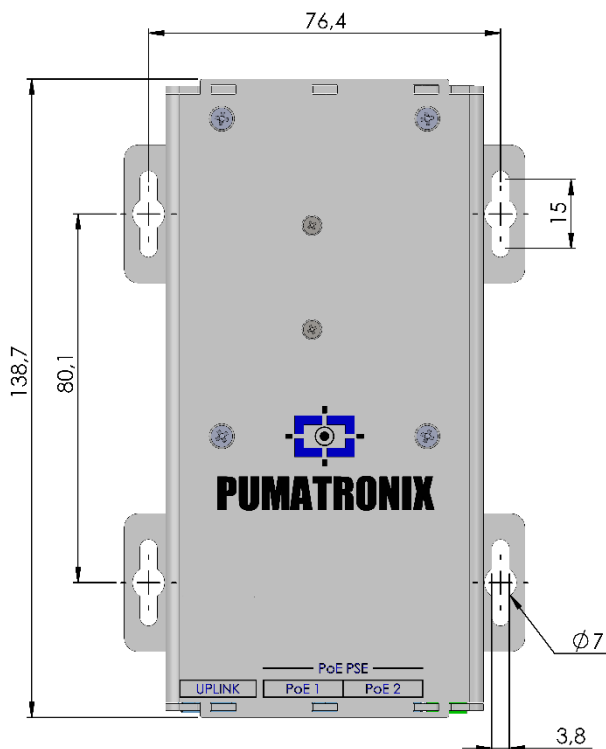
VISTA SUPERIOR COM DIMENSÕES
